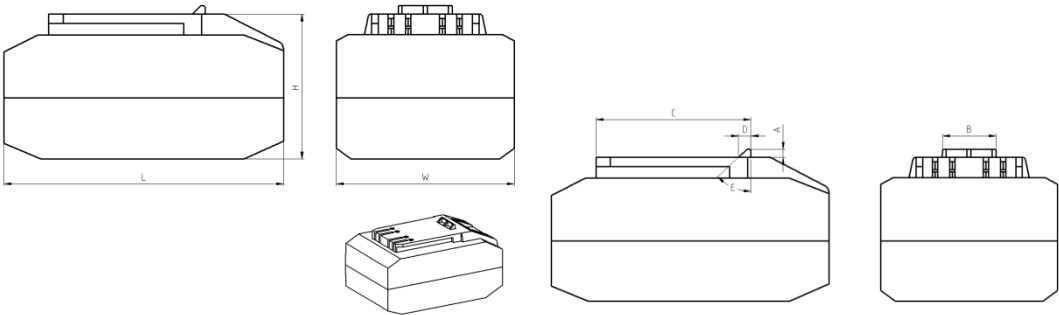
电池包外形尺寸图 3 接口锁扣尺寸
